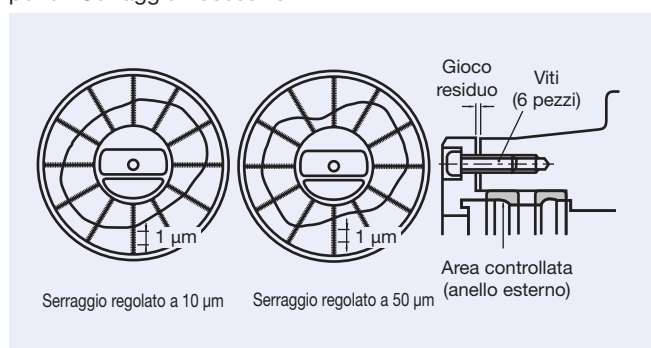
Deformazione dell'Anello Esterno di un Cuscinetto a Due Corone di Rulli Cilindrici per un Serraggio Eccessivo
